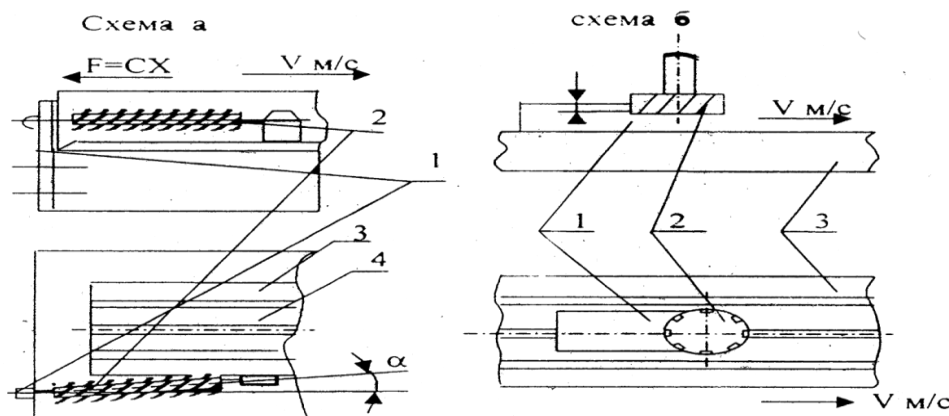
Схема а: 1-кронштейны; 2-пружина; 3-стол станка; 4-станина;
